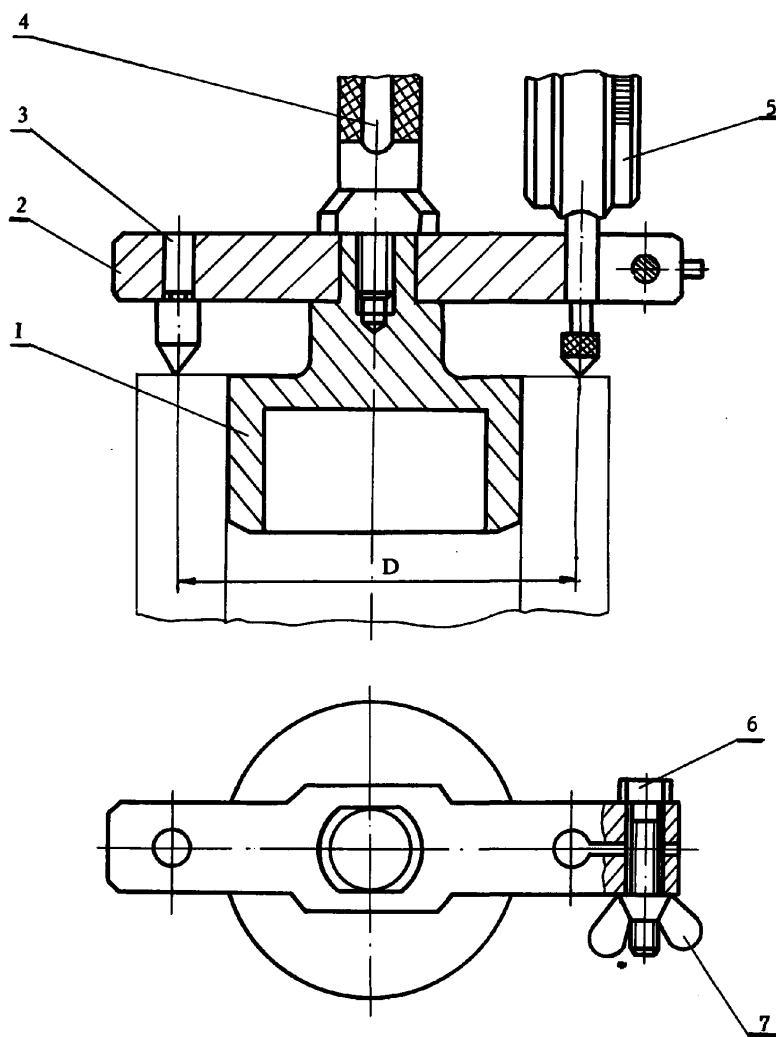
Знімний контрольний пристрій для перевірки биття торця диска
